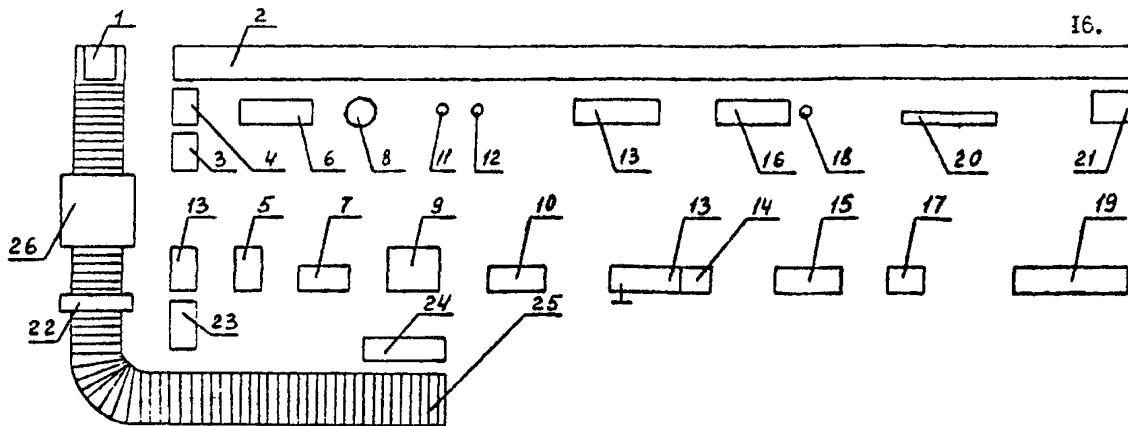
Типовая схема планировки рабочего места сборки двигателя
